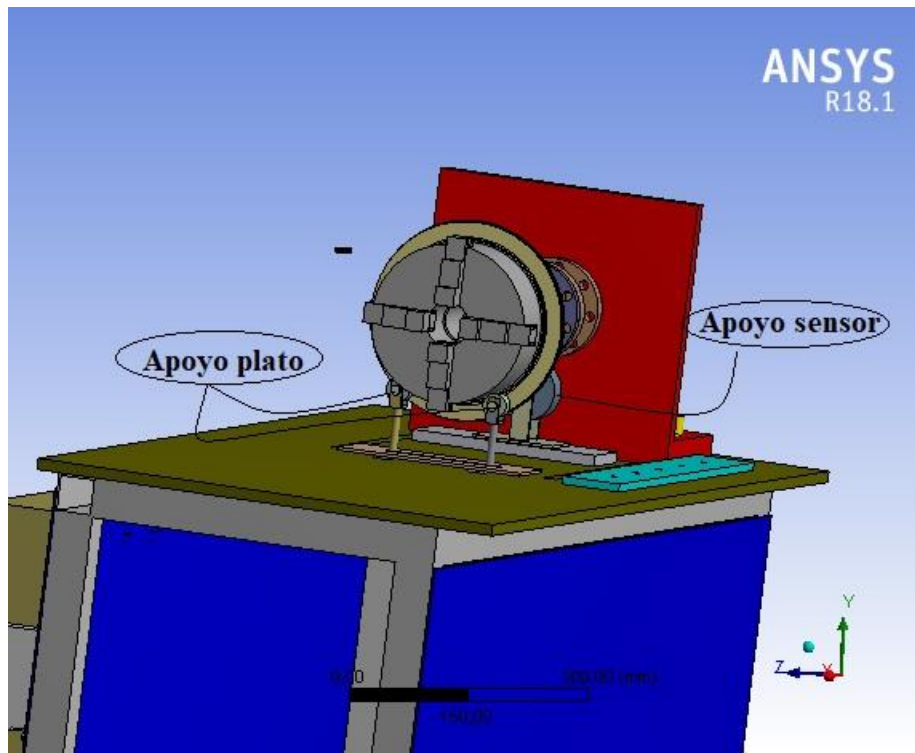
Vista preliminar de la instalación de los apoyos. Fuente: Elaboración propia.
